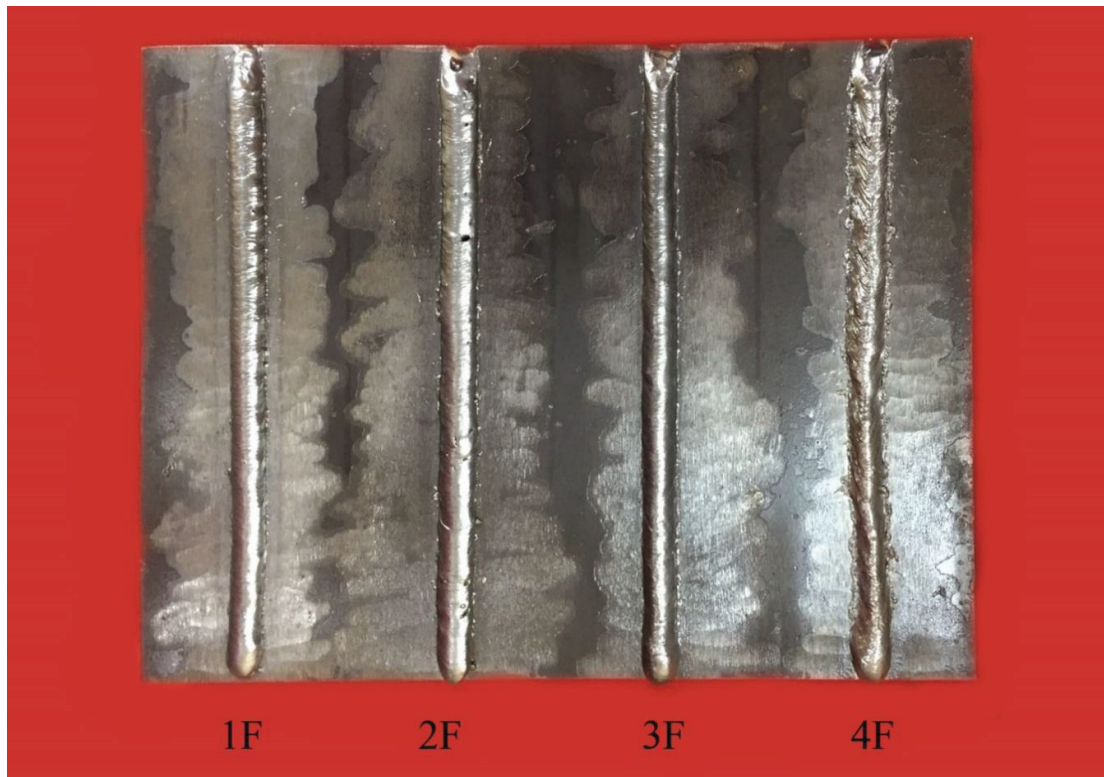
Depósitos de soldadura,  $\varnothing 0,9$  mm, stick out 10 mm y protección  $CO_2$
